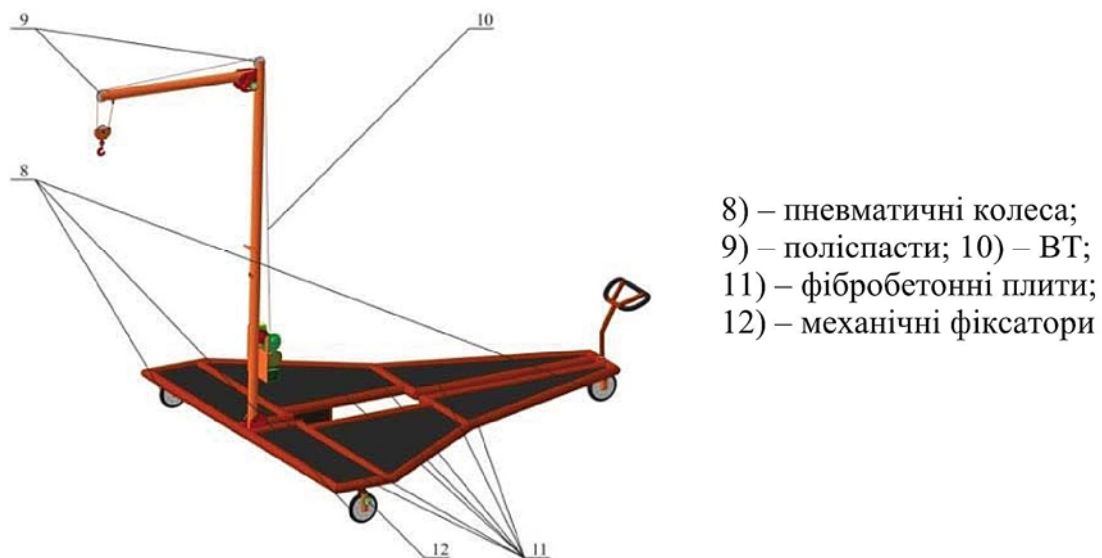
3D модель конструкції ВЛ на колісній базі (вид збоку)
